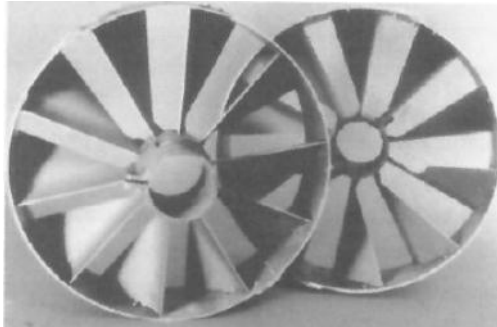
Стабилизатор пламени форсунки из сплава Incoloy MA 956 [8]
